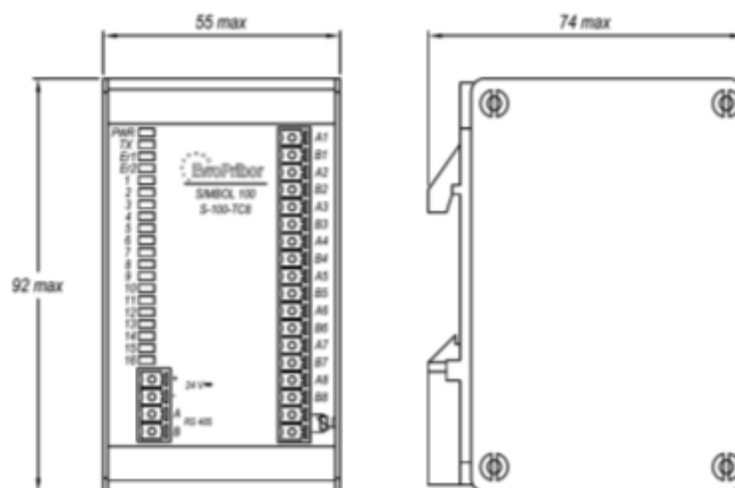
Габаритные размеры модулей контроллера Simbol-100
